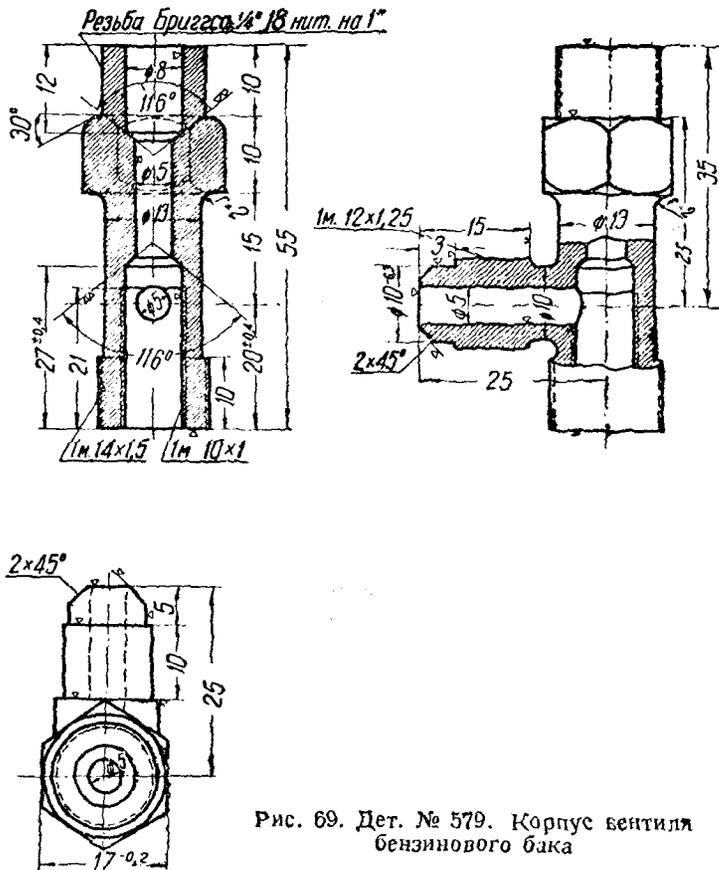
Дет. № 579. Корпус вентилля бензинового бака
